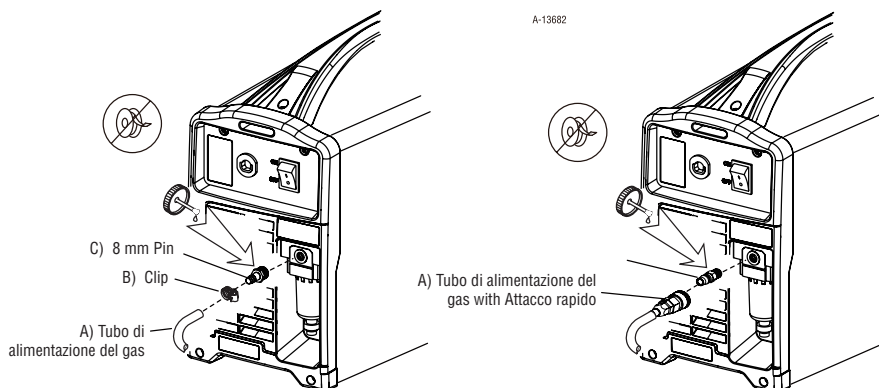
Connessione gas all'ingresso dell'aria compressa.
